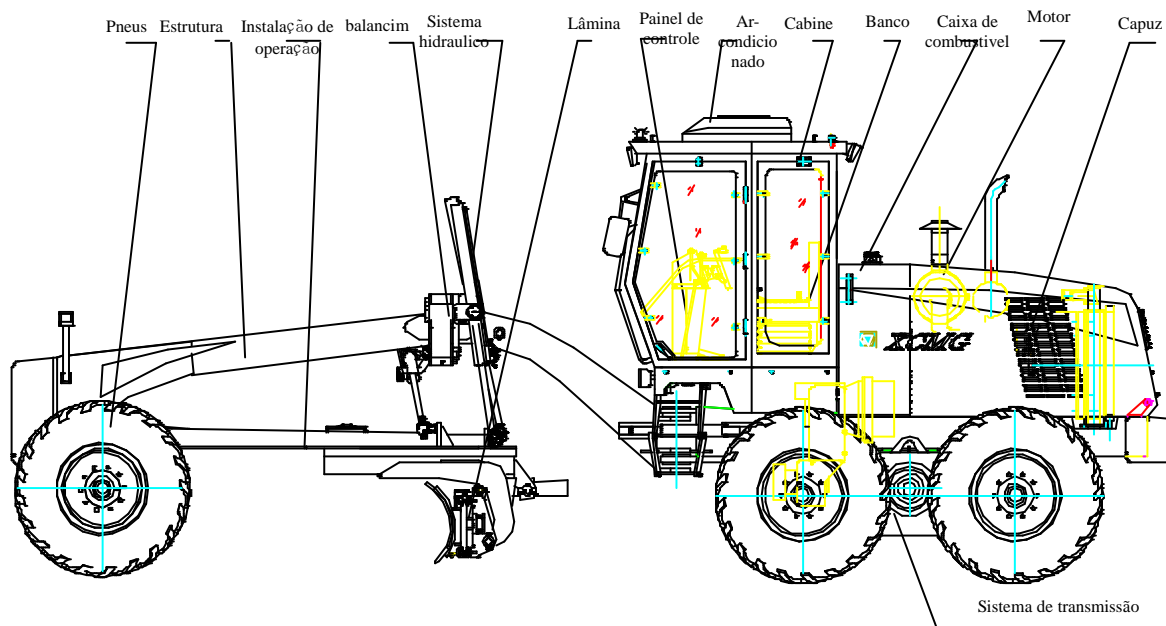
Desenho do esboço geral e nomes parte das motoniveladora GR1803BR
